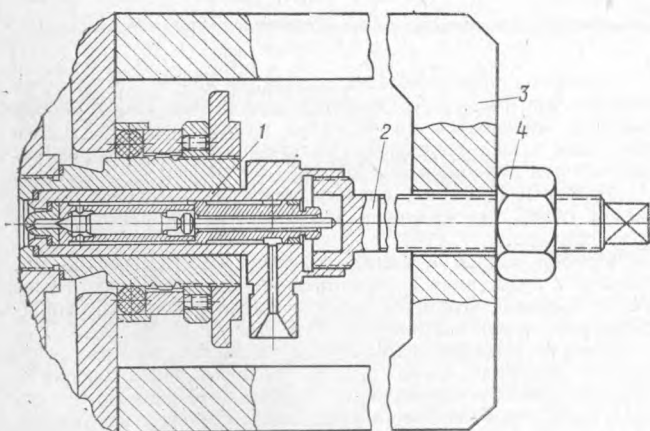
Приспособление для извлечения закоксованной форсунки из адаптера гильзы цилиндра:
